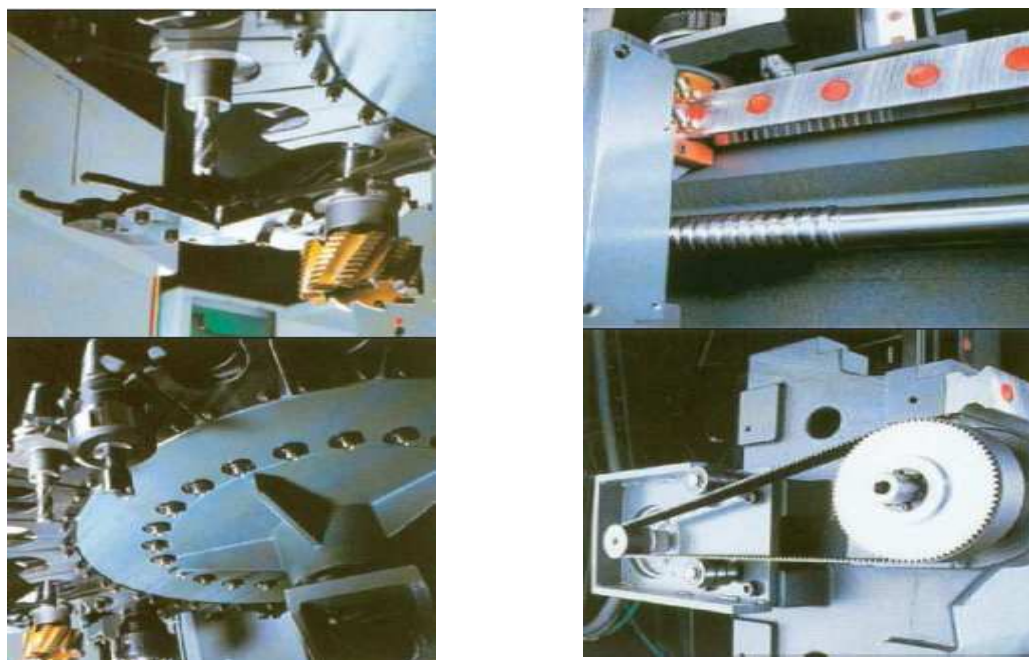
Ukázka provedení frézky FGS CNC s celokabinovým krytem [10]
